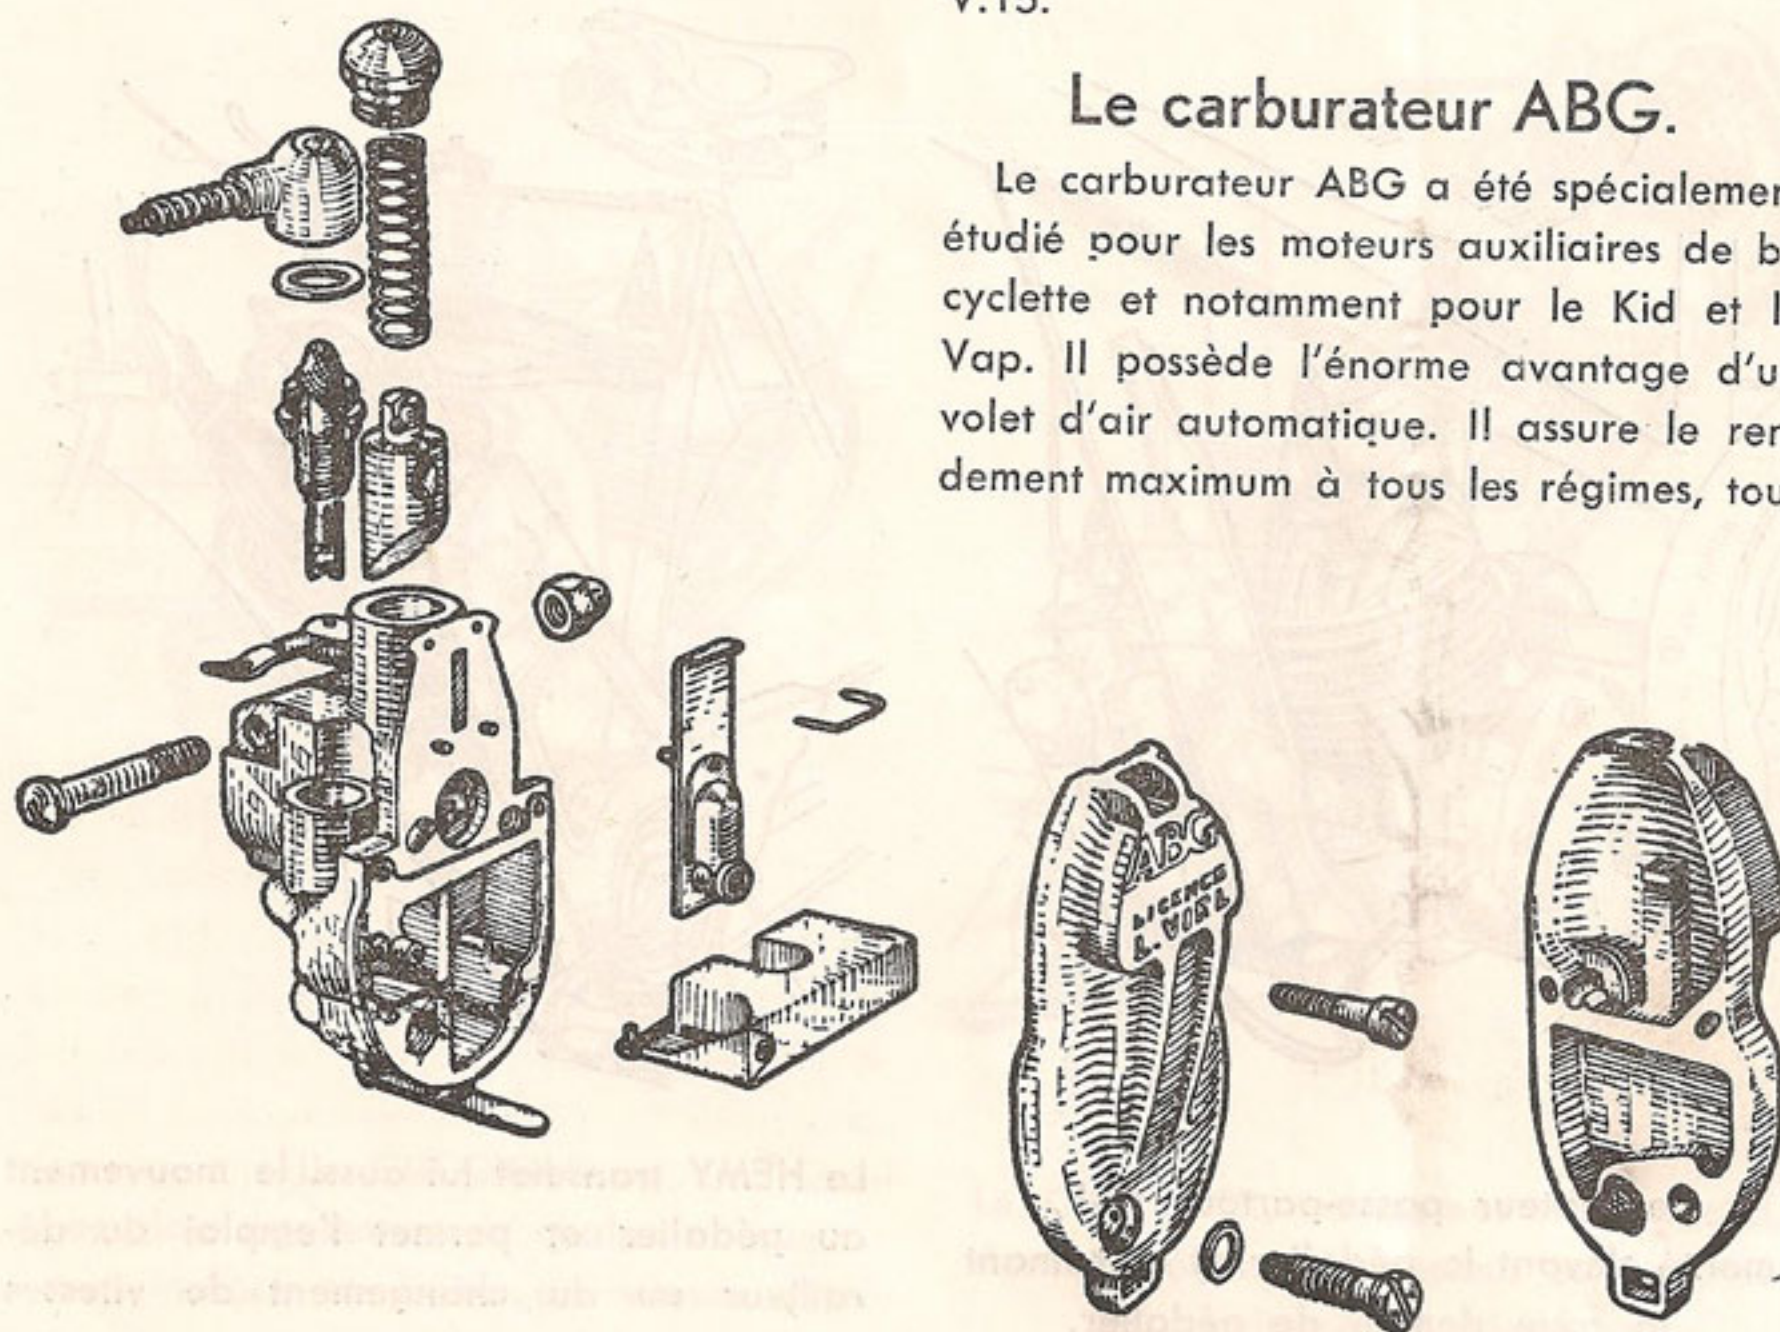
VUE ECLATEE DU CARBURATEUR ABG.
